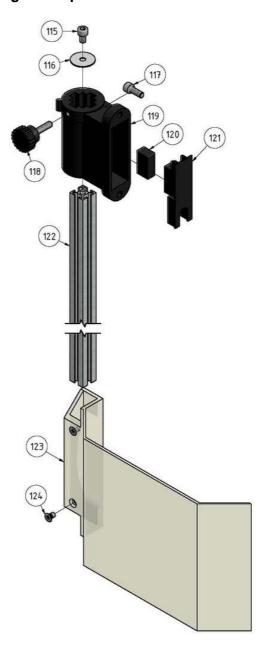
Fräsfutterschutz - Milling chuck protection
